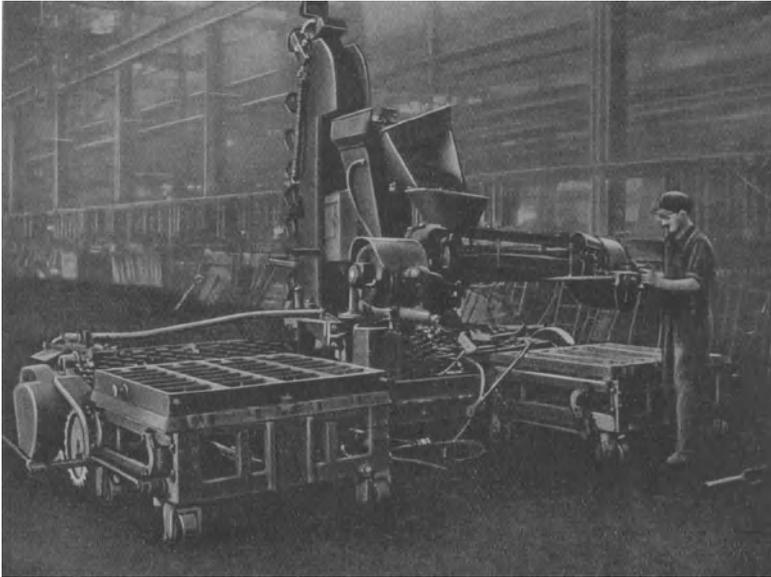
Trecker-Sandschleuderer mit Abhebemaschinen für Radiatorenformen.
